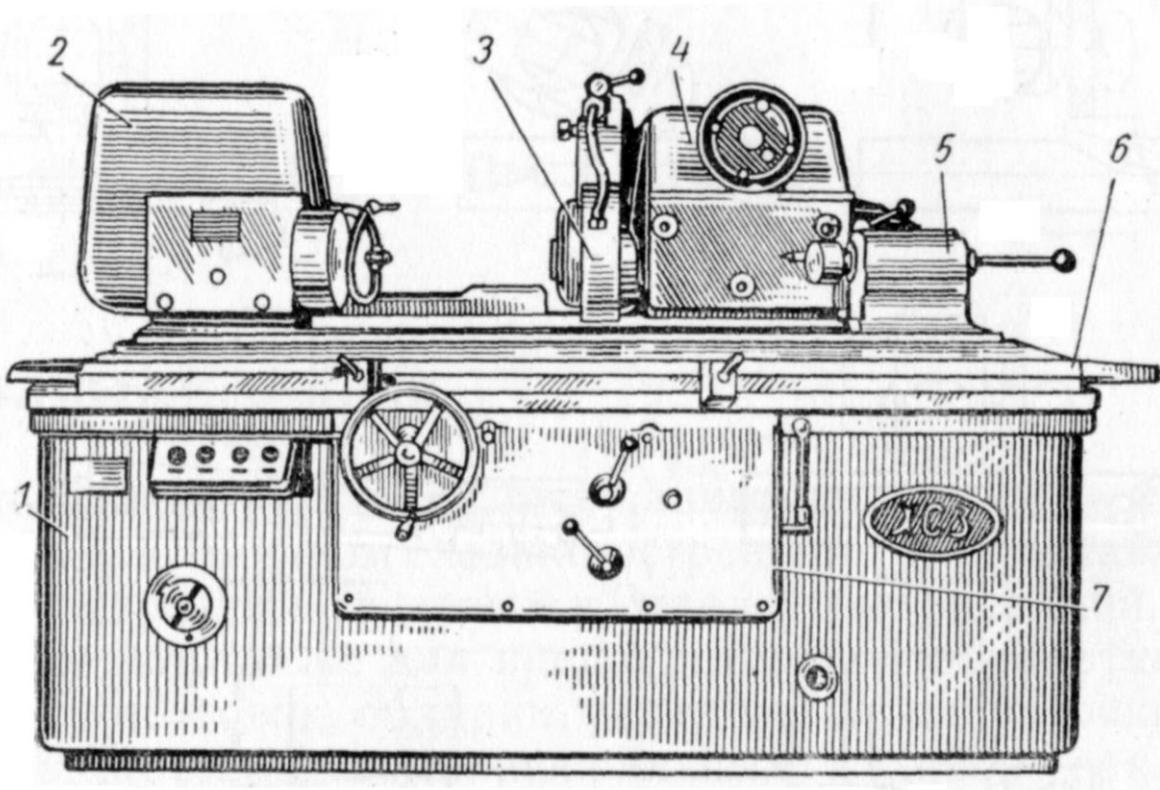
внешний вид круглошлифовального станка модели 3151
